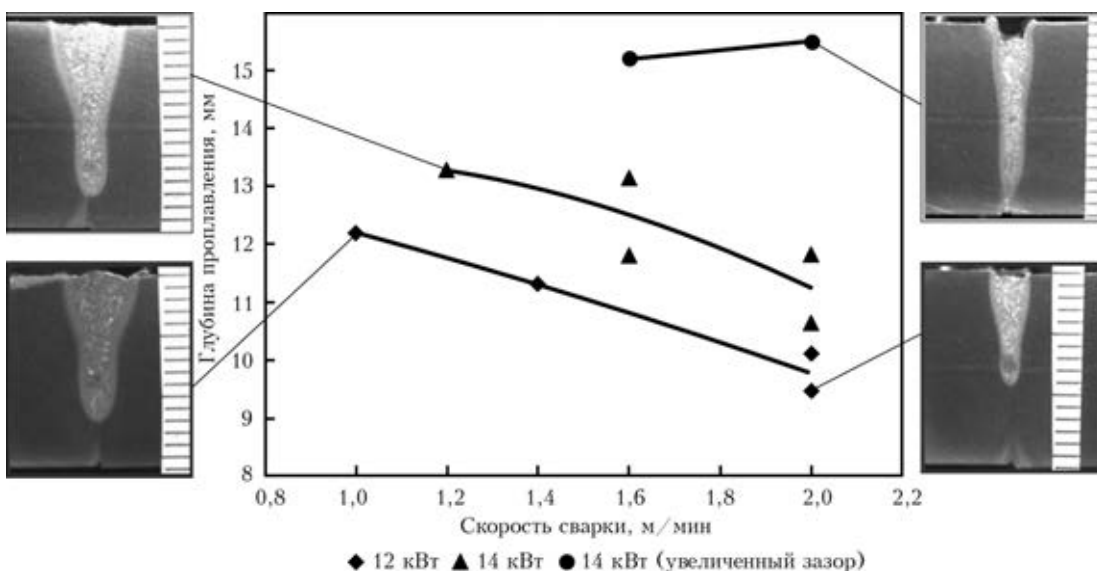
Влияние различных параметров лазерной сварки на глубину проплавления образцов (Ст3, $t = 16$ мм)
